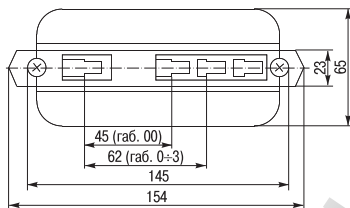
Габаритные размеры рукоятки для смены плавкой вставки
